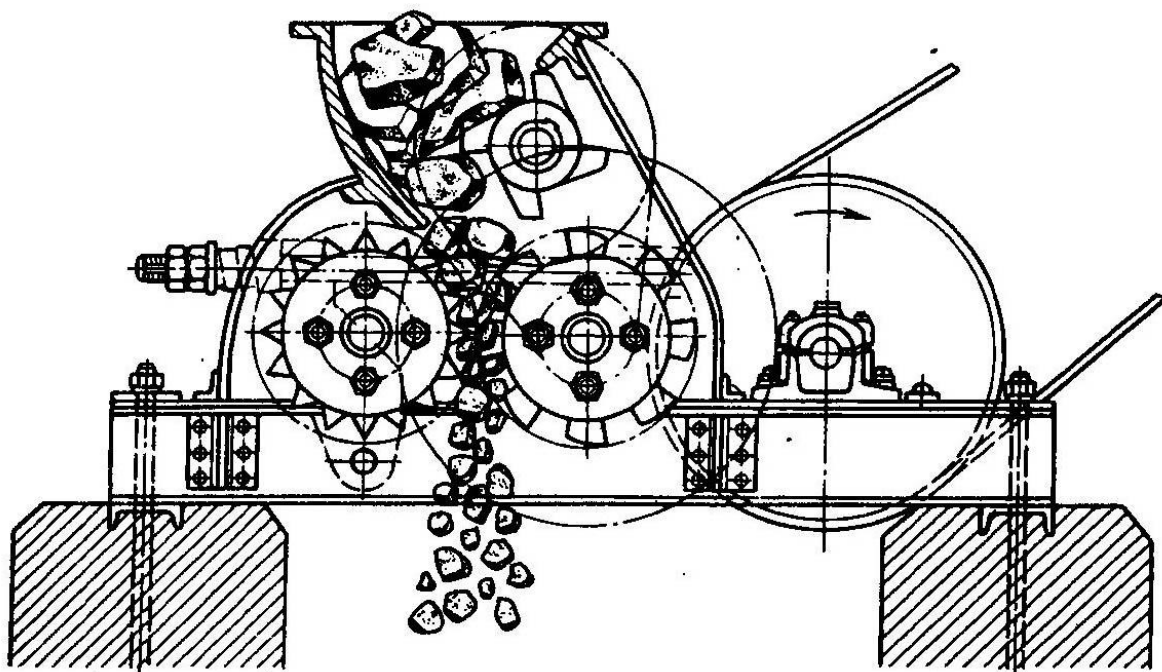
Трехвалковая дробилка для пород малой прочности
